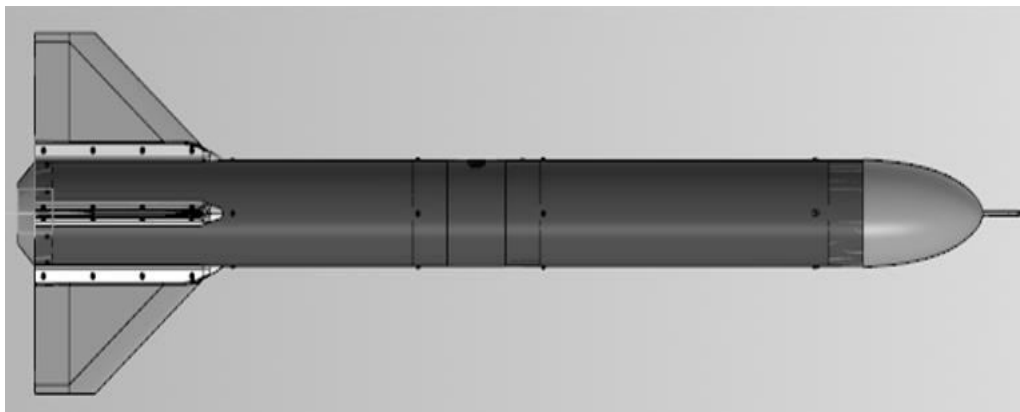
Ракета-носитель измерительного оборудования. Общий вид
